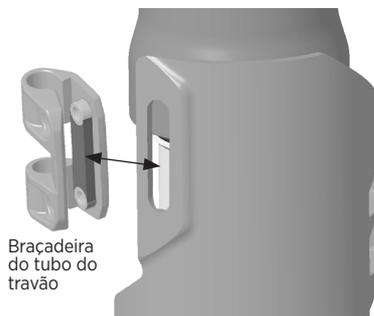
Instalação da braçadeira do tubo do travão na proteção inferior do garfo
